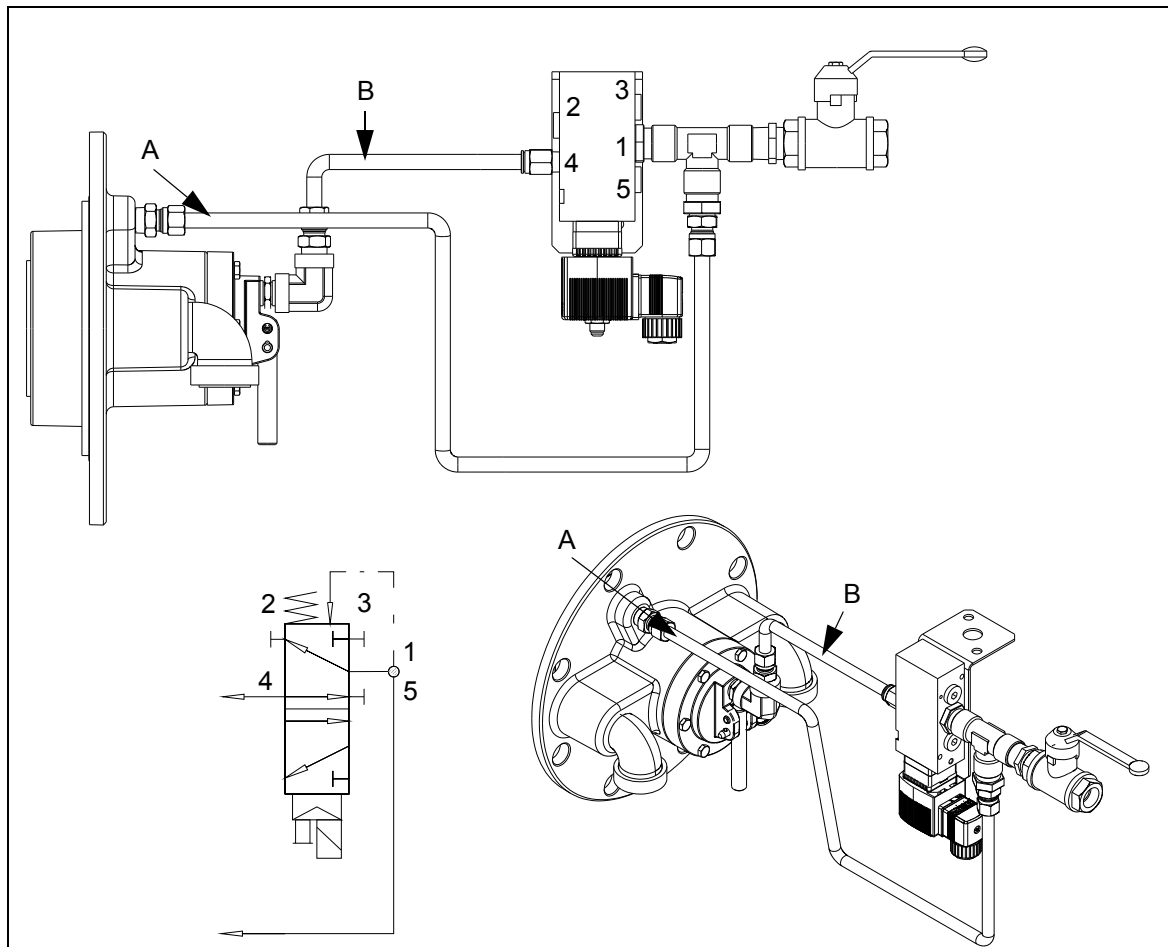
Pneumatische Anschluss eines 5/2-Wege Ventils - ISO-metrische Ansicht
